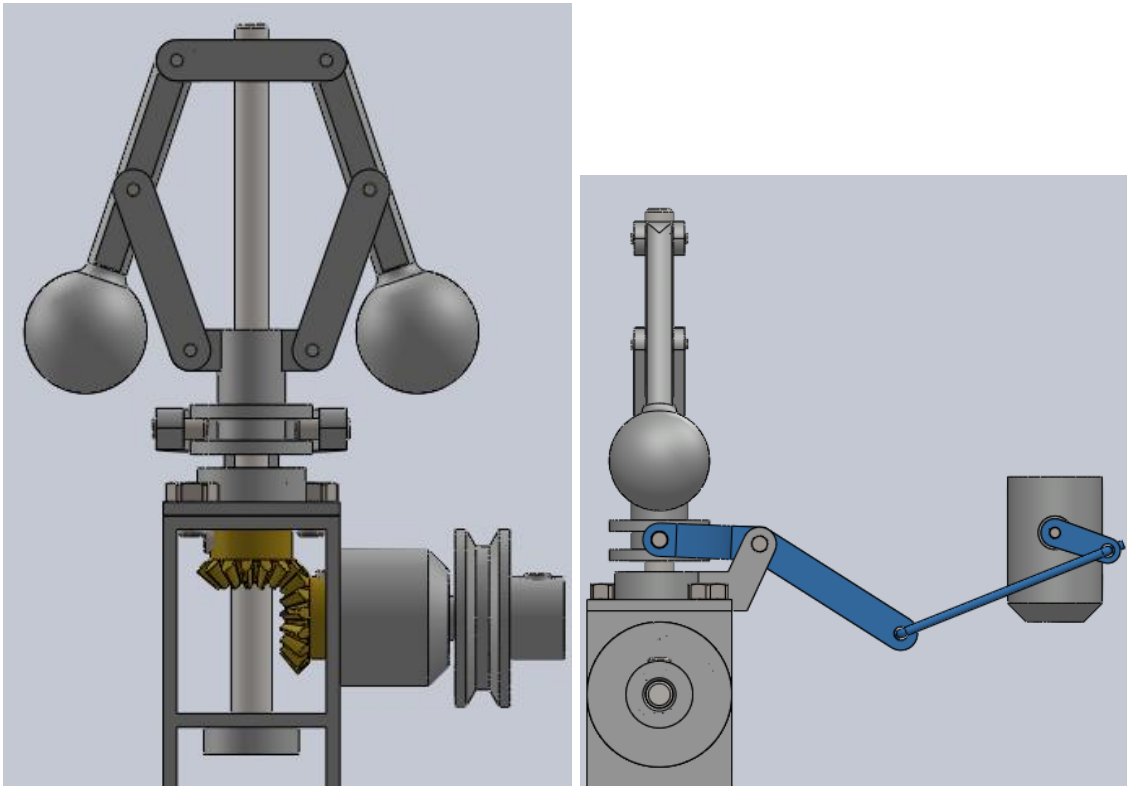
Vista frontal de regulador centrífugo diseñado (izquierda) y vista lateral de regulador con el sistema de barras que acciona la mariposa en azul (derecha).
